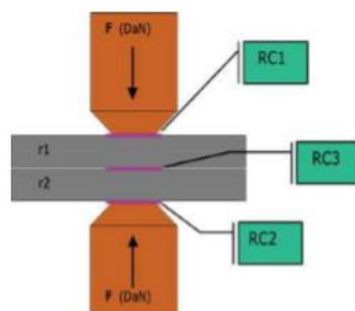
Mécanisme de formation de point de soudure de soudage par point. [4]
